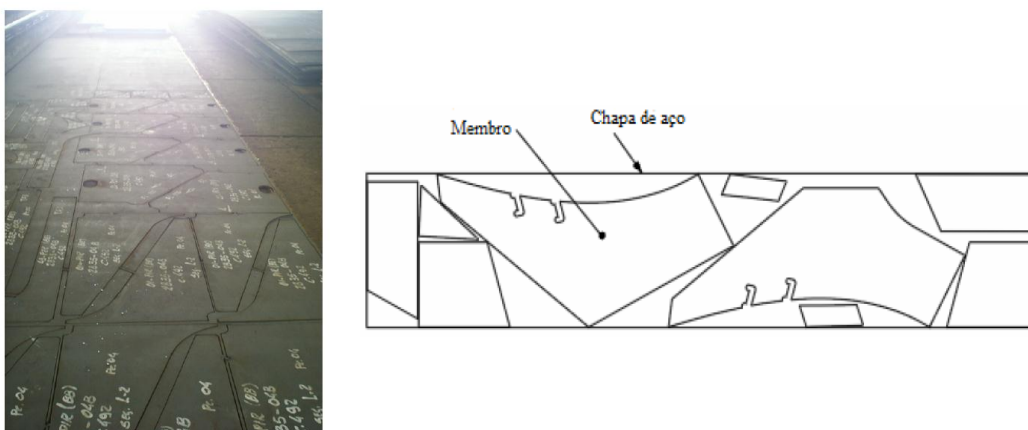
Plano de corte em chapas de aço (MELO, 2012)
